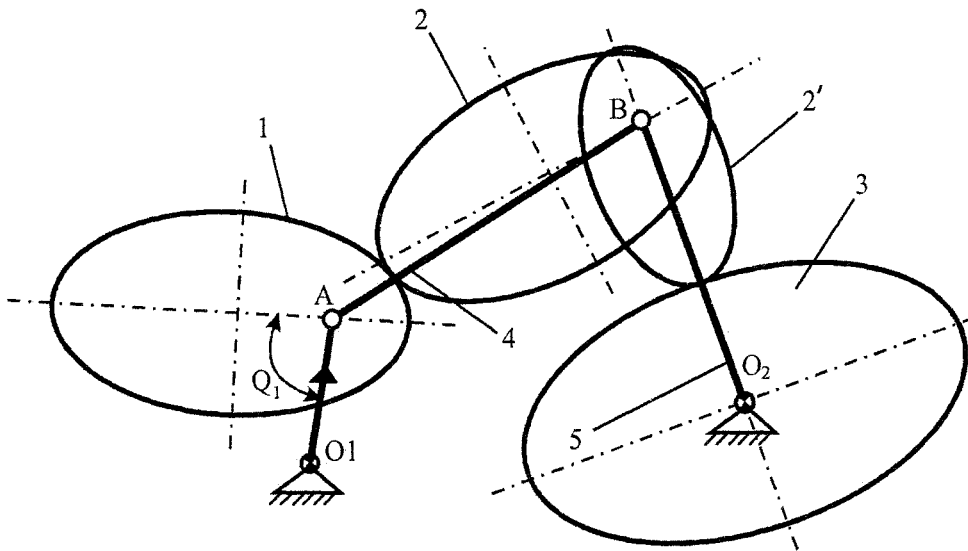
Схема зубчато-рычажного механизма периодического движения по схеме третьего типа для двухпозиционного револьверного стола
